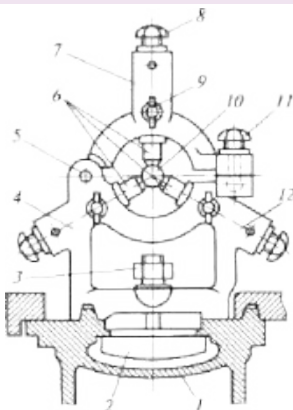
Елементи нерухомого люнета: 1 — станина; 2 — сухар; 3 — гайка; 4, 12 — стойки, 5 — вісь; 6 — кулачки; 7 — кришка; 8, 9, 11 — гвинти; 10 — заготовка
